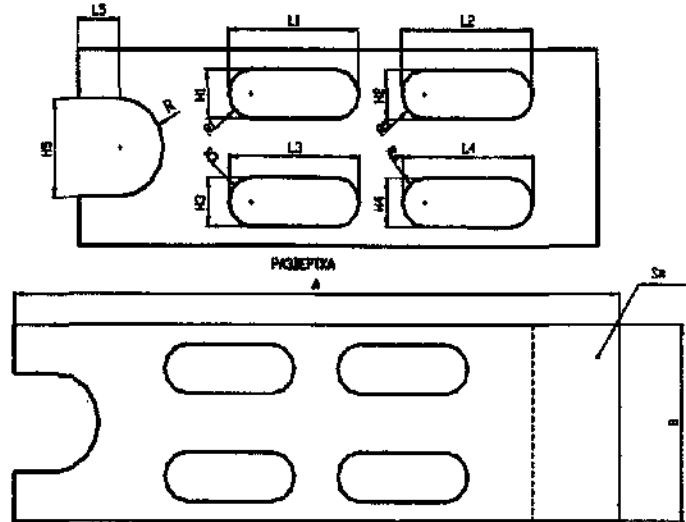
Чертеж комплексной детали одной из групп класса «Листовые детали»
